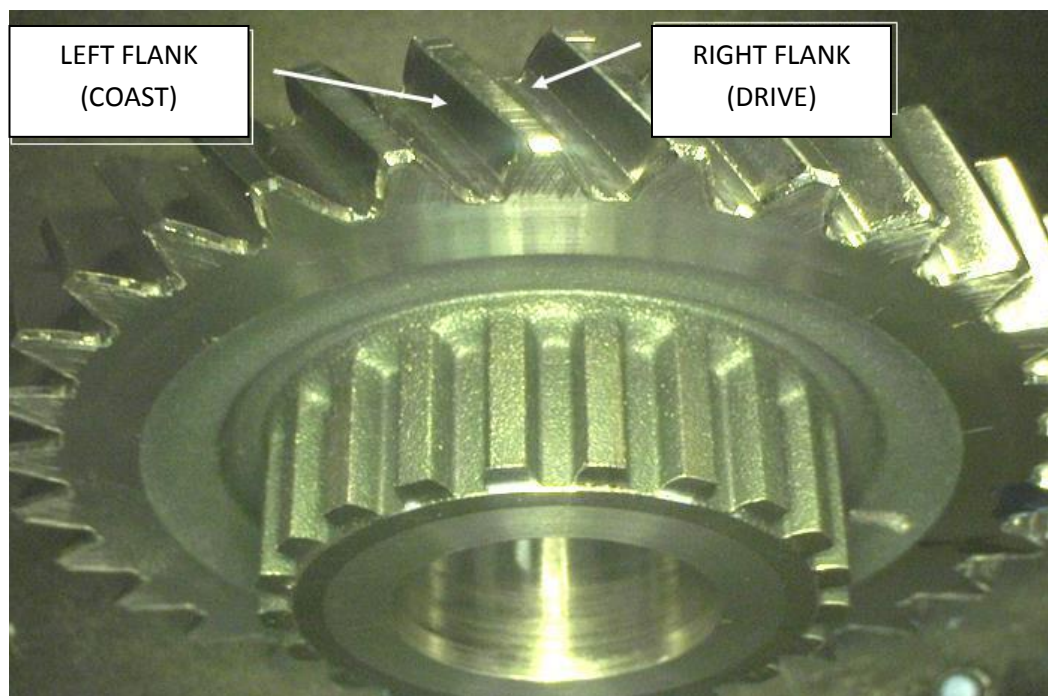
Engrenagem com demonstração do lado funcional (Right Flank – Drive).
